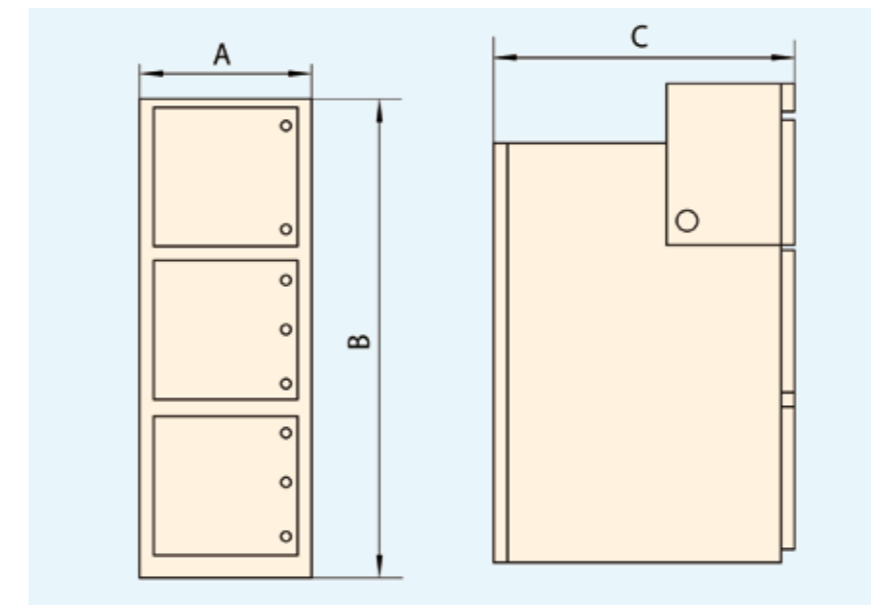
Внешний вид KYN28A-12(Z)(GZS1)
